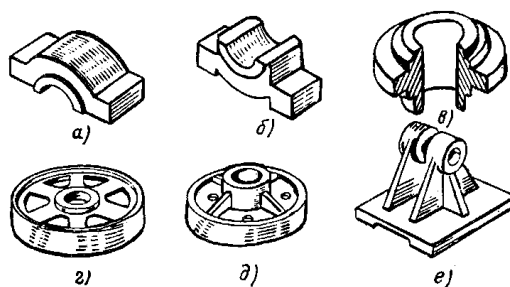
Отливки 2-й группы сложности: а - крышка подшипника; б - корпус подшипника; в - ступица; г - зубчатое колесо; д - ролик; е - кронштейн
